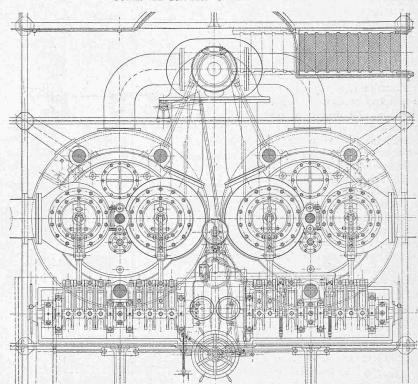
Grundriss (Schnitt zwischen den Cylindern) 1:50.
